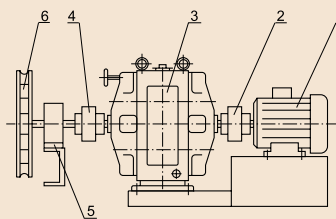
Привод цепного конвейера на базе цепного вариатора:
